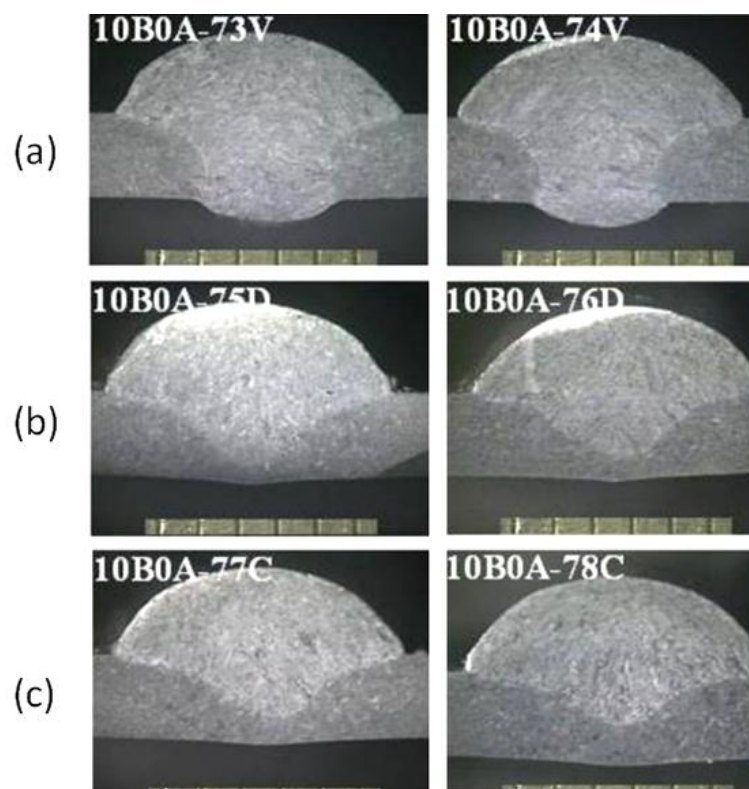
Cordões de solda [26]. (a) 20Hz; (b) 10Hz; (c) 5Hz.
